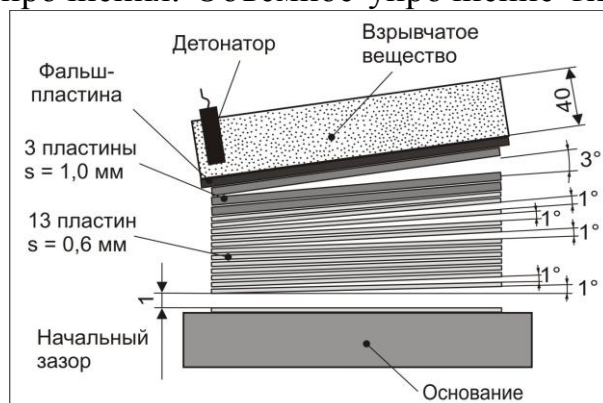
Схема сварки взрывом 16-слойного композита типа «BT1-0 - BT1-0»
